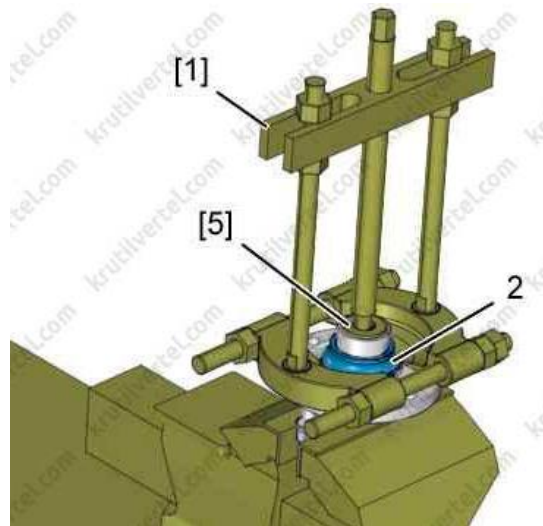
Зняття внутрішньої обойми підшипника:
